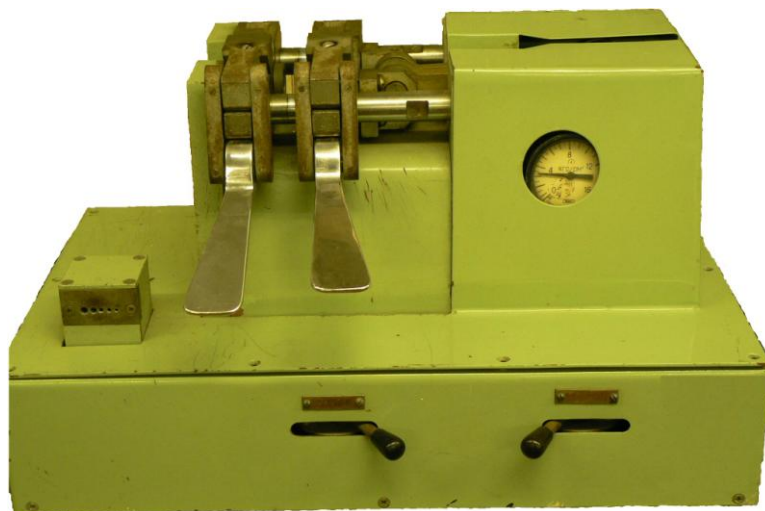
Внешний вид машины типа МСХС-5-3
